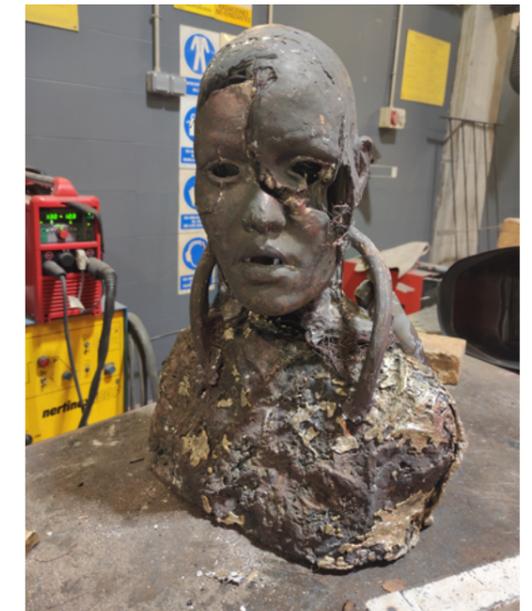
Diego Vidal. Todas las partes soldadas.
